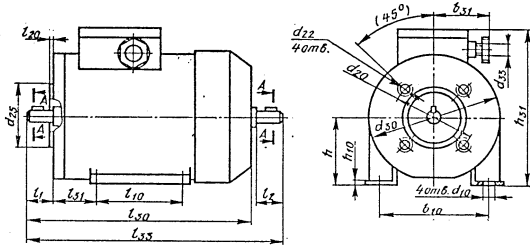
Габаритные, установочные и присоединительные размеры двигателей исполнений 1М2181, 1М2182
